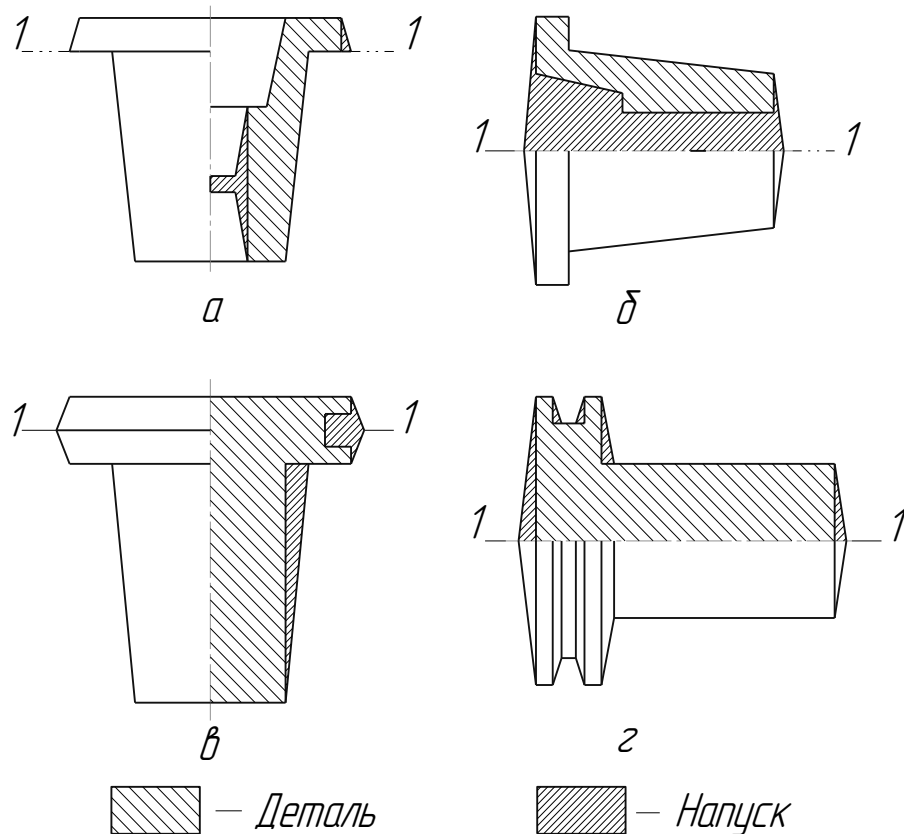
Вплив розташування поверхні рознімання штампу (1–1) на форму поковок
